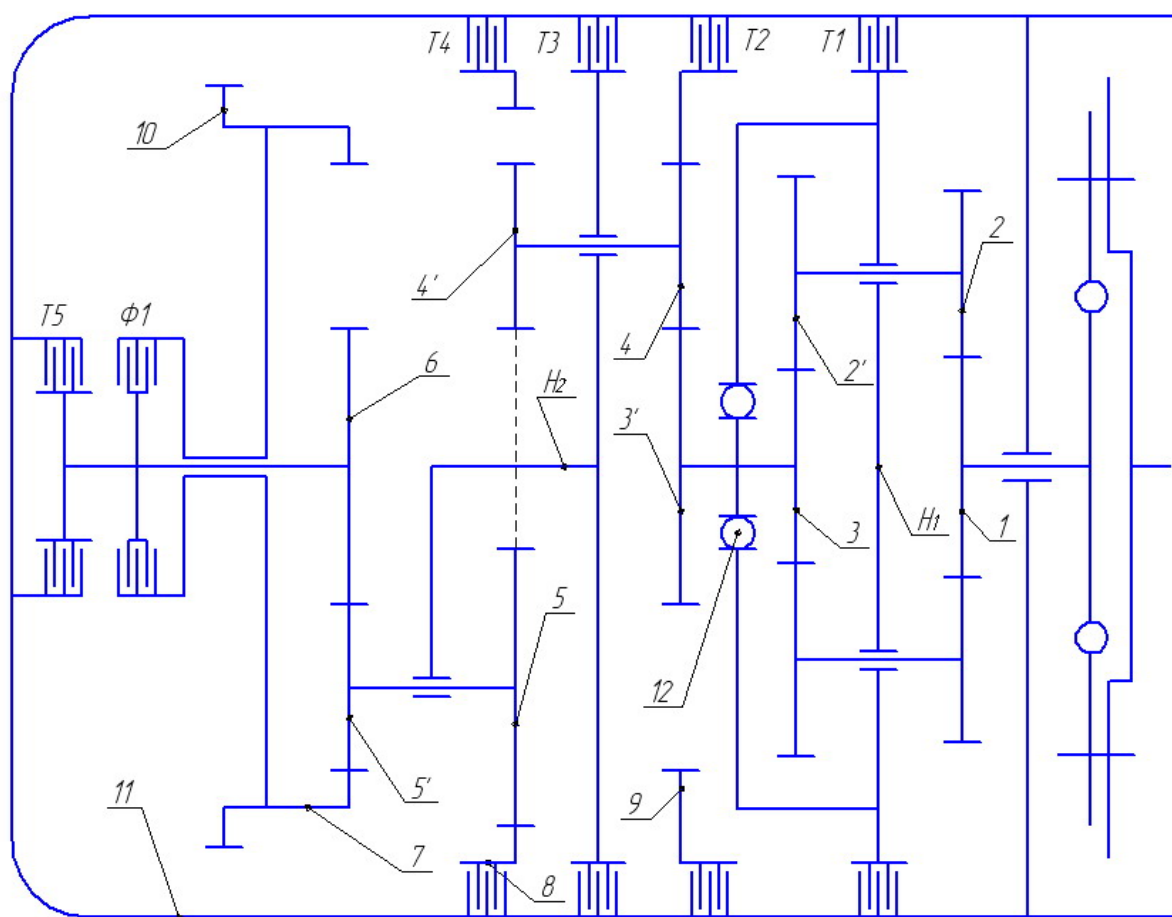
Кинематическая схема коробки передач на основе УМДМ
